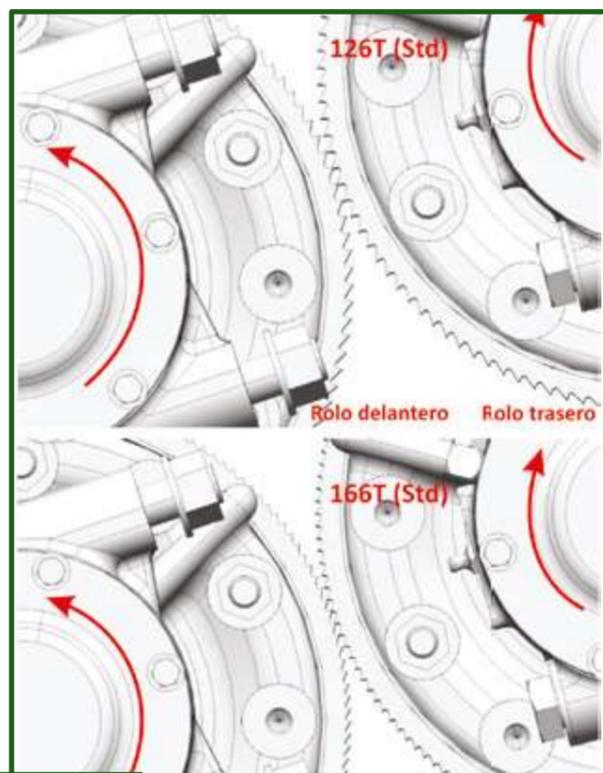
Diferentes diseños de rodillos que pueden ser cambiables, para permitir el quebrado del sorgo. T (dientes).
